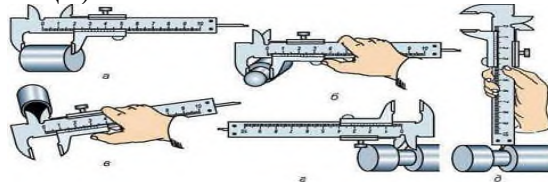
Вимірювання та контроль розмірів деталей штангенциркулем
